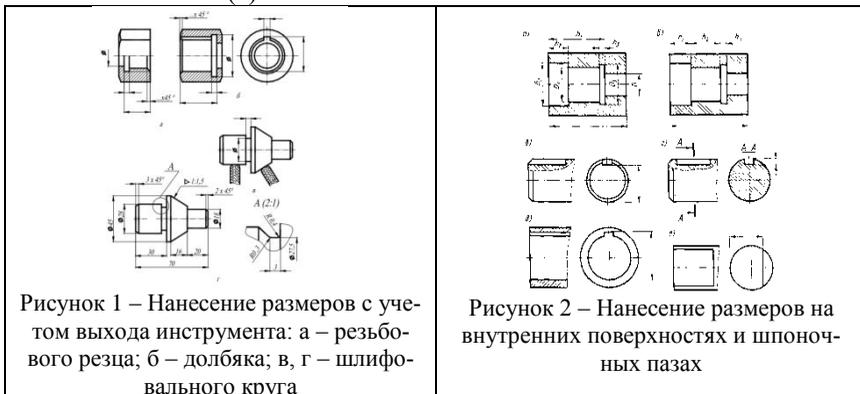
Нанесение размеров с учетом выхода инструмента: а – резьбового резца; б – долбяка; в, г – шлифовального круга
